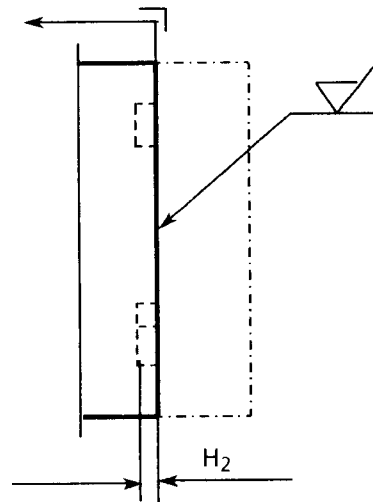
Inre defekter i snittad (bearbetad) yta/Internal defects in sectioned (machined) area
